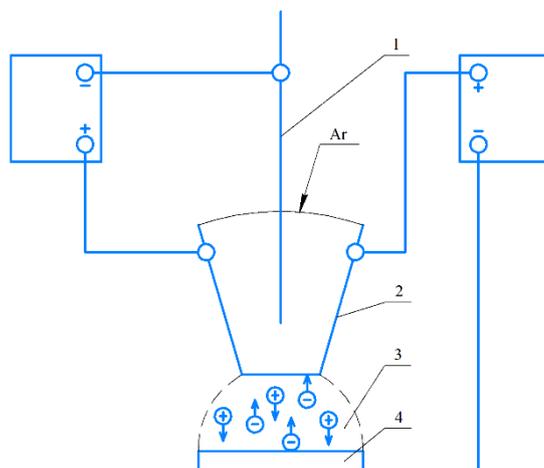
Схема микроплазменной сварки на обратной полярности
